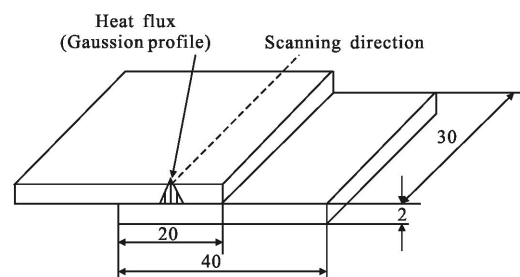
PC 焊接试验焊接形式及样品尺寸
